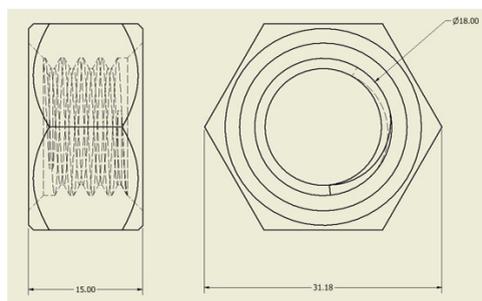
Tampak Luar Design Baru Komponen Poros Penghantar
